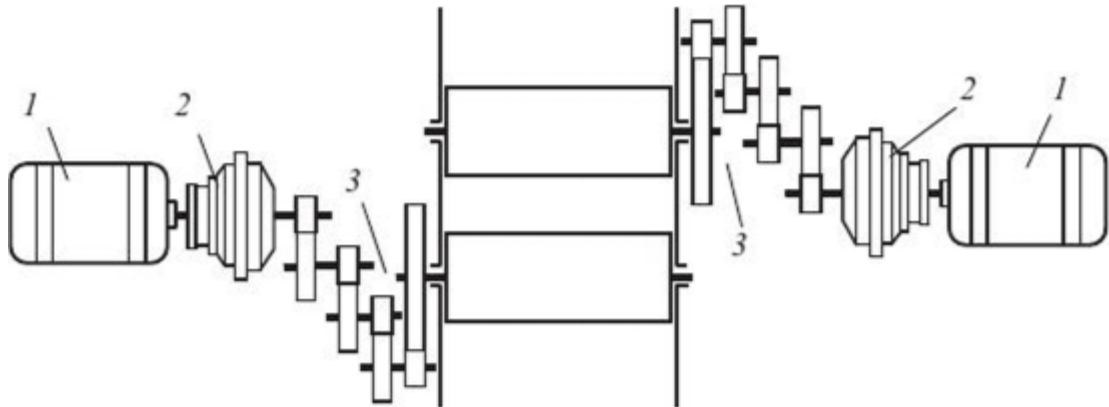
Кінематична схема двобарабанного приводу із незалежними приводними електродвигунами: 1 – електродвигун; 2 – гідromуфта; 3 – редуктор; Б1 та Б2 - приводні барабани [46].
